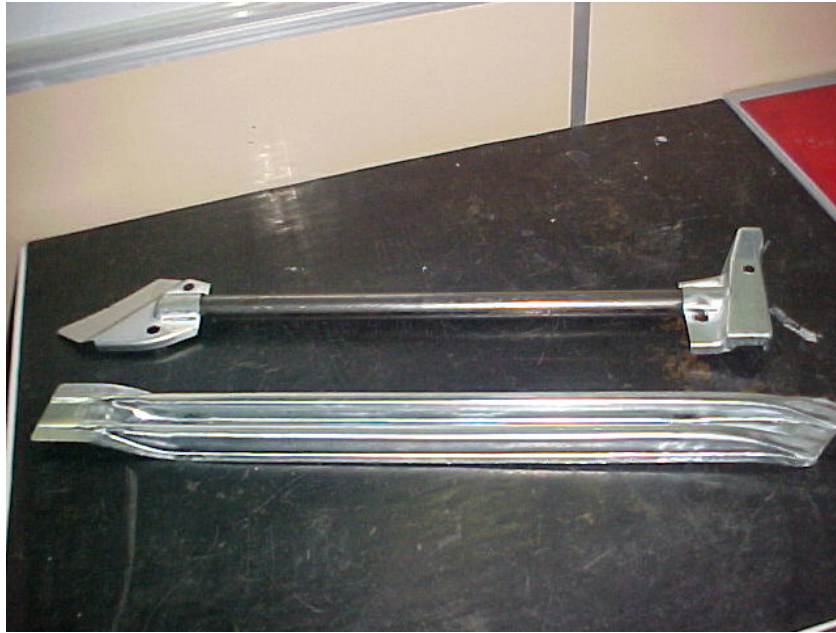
Barras de proteção lateral tubular e estampada antes do ensaio de corrosão
